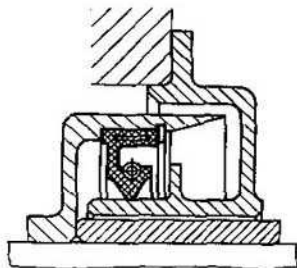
Empaquetadura combinada: disco deflector, manguito de empaque
